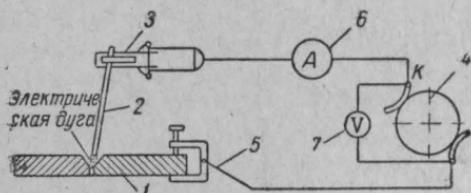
Схема ручной электродуговой сварки металлическим электродом:
